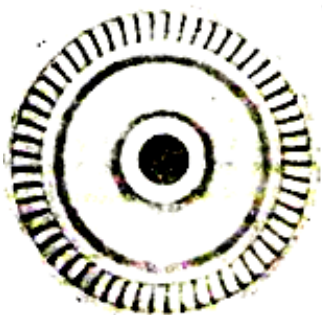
Отливки из конструкционных сталей, жаропрочных алюминиевых и медных сплавов изготовленные по выплавляемым сплавам.
